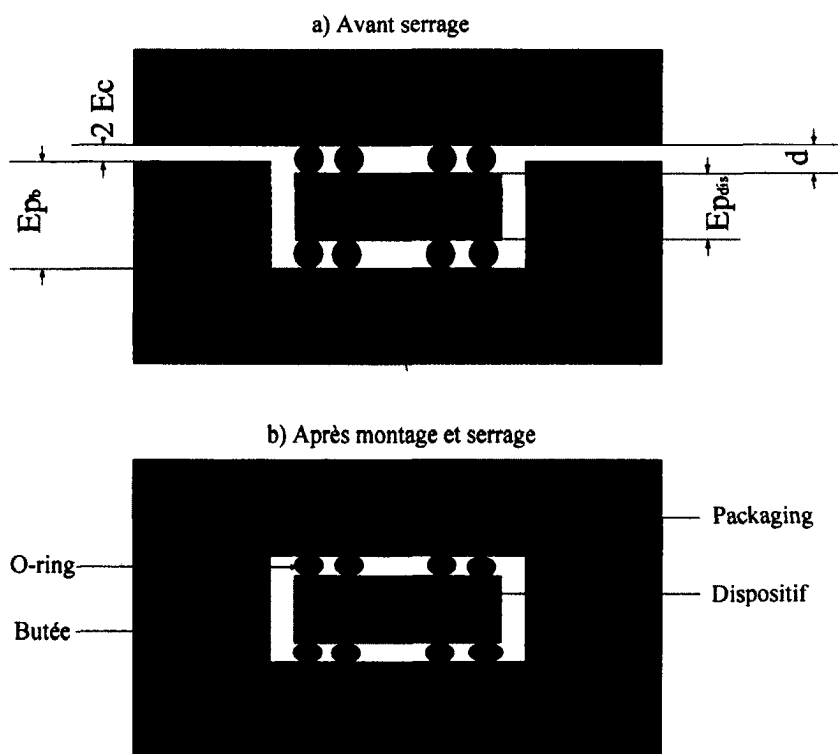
Serrage des *O-ring* par la méthode de la butée
